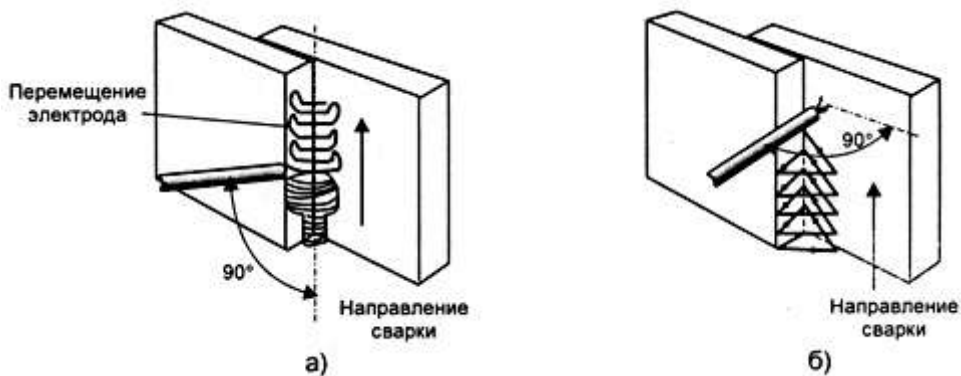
Положение электрода при сварке нахлесточного соединения в вертикальном положении снизу вверх многопроходным угловым швом и однопроходным угловым швом
